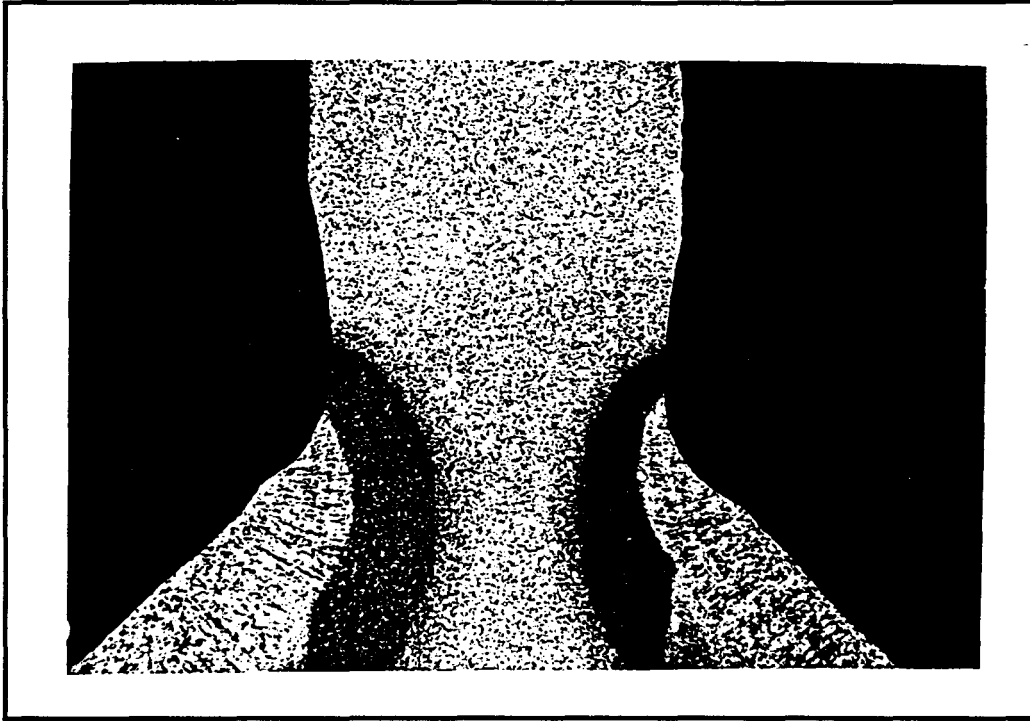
Pieds de cordons de soudure écriquetés [30]
